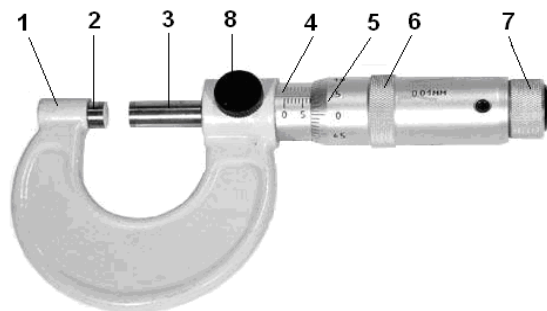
Мікрометр гладкий: 1 – скоба; 2 – нерухома вимірювальна п'ятка; 3 – мікрометричний гвинт; 4 – стебло; 5 – кругова шкала барабана; 6 – барабан; 7 – тріскачка; 8 – стопорний гвинт або гайка
